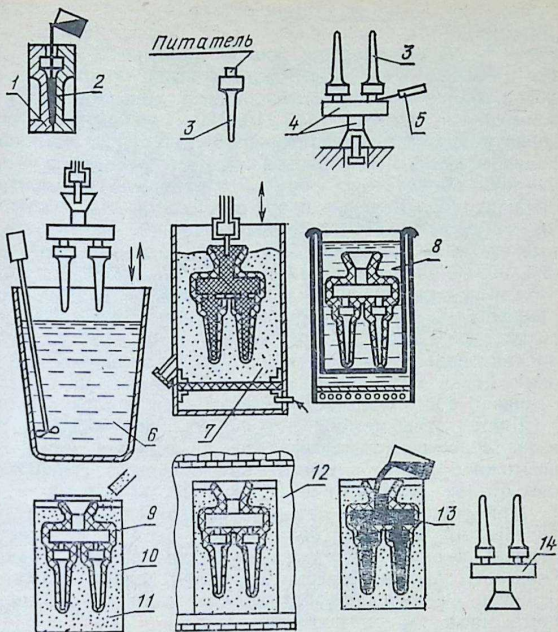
Изготовление отливок по выплавляемым моделям:
